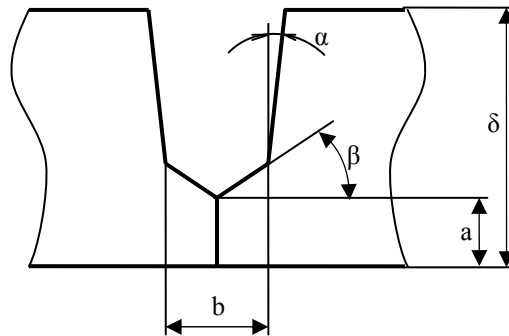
Схема выполнения разделки кромок для многопроходной лазерно-дуговой сварки.
